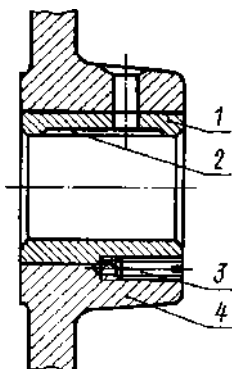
Неразъемный подшипник, встроенный в станину машины:
